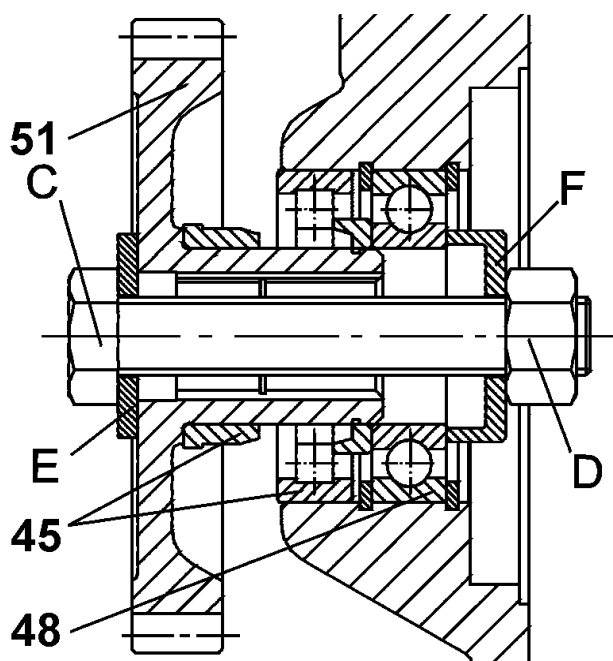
В.13. Втискивание ведомой шестерни в подшипники
